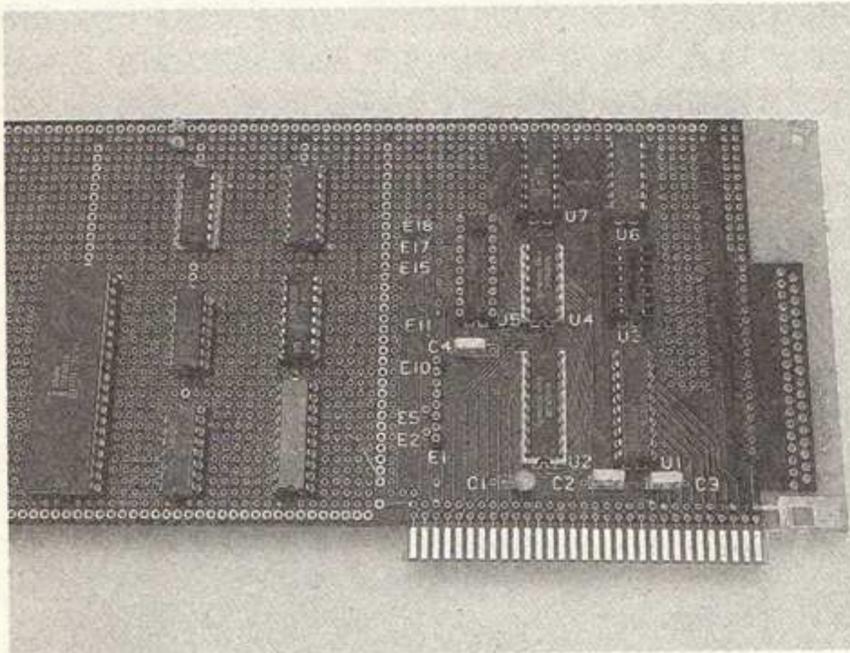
Montaje mediante hilo enrollado sobre tarjeta de prototipos IBM-PC.
